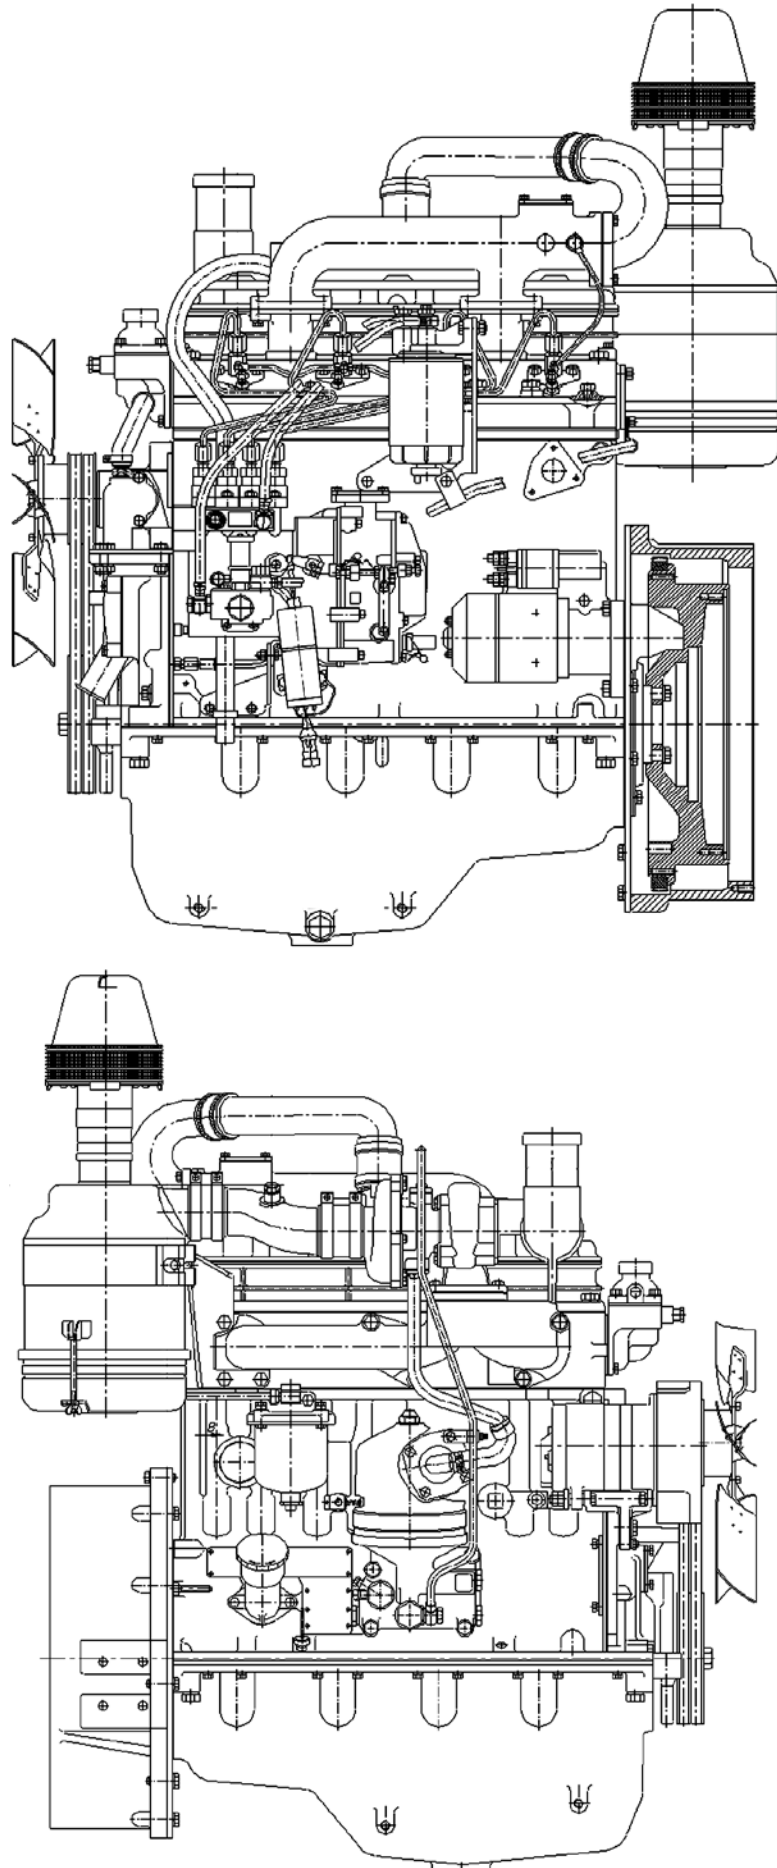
Общий вид двигателя Д-246.2, Д-246.7.
